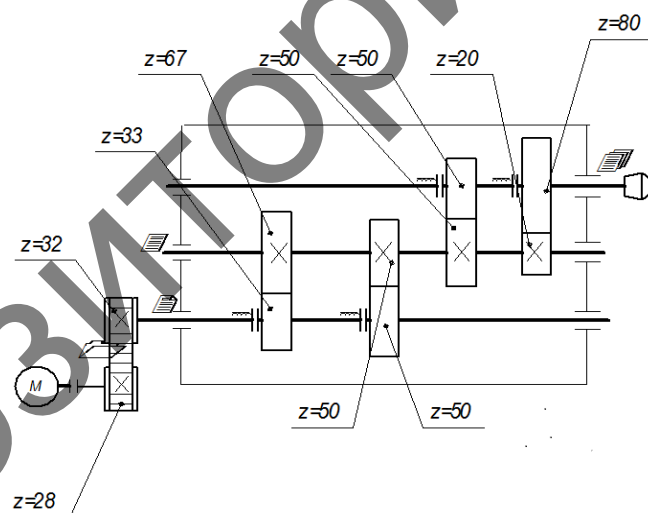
Кинематическая схема модернизированного привода главного движения станка 1П367
